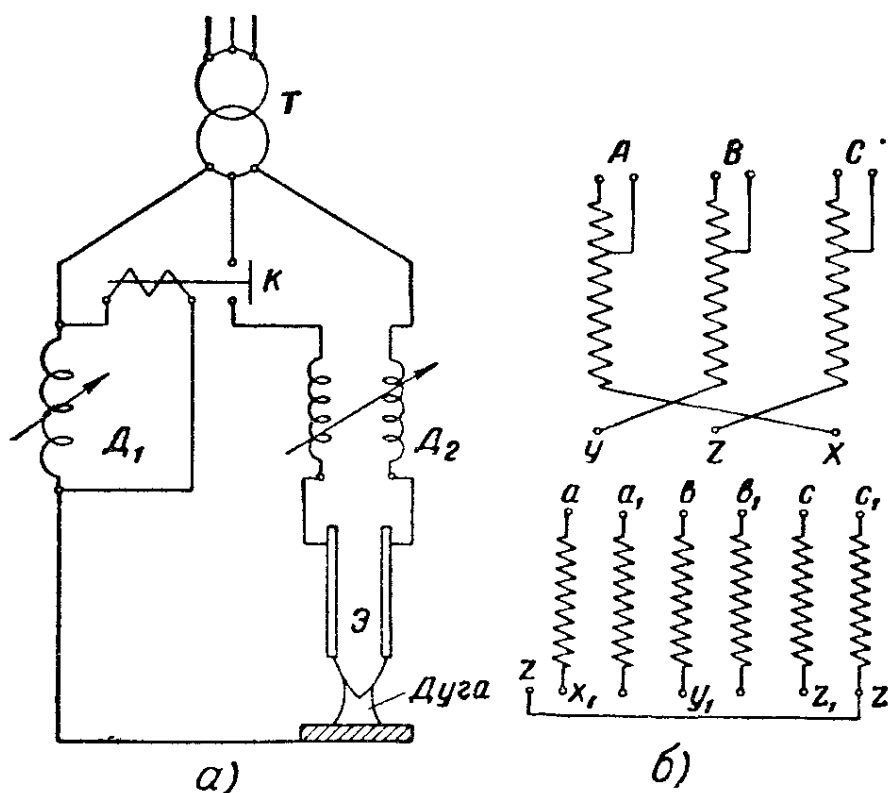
Схема включения трансформатора ЗСТ и регулятора при сварке трехфазной дугой:
